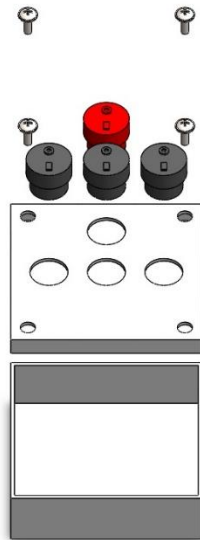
Vista explosionada panel de control. Fuente: Propia.
